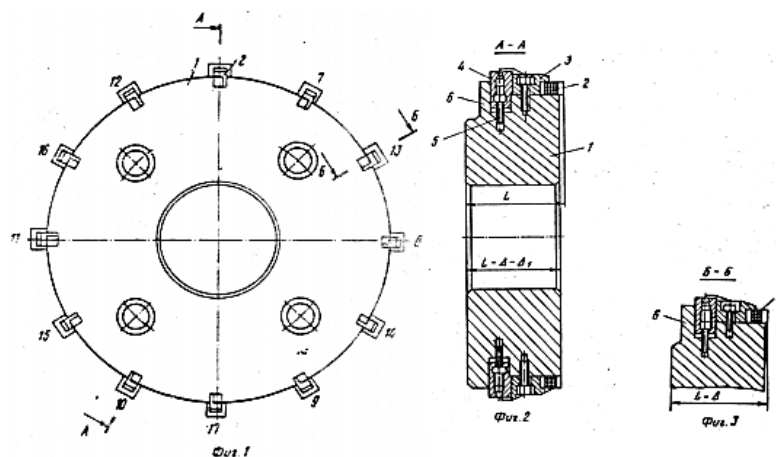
Торцева фреза по а. с. 623311 Рис.1.19. МКИ В 23 С 5/06 17 [3]
